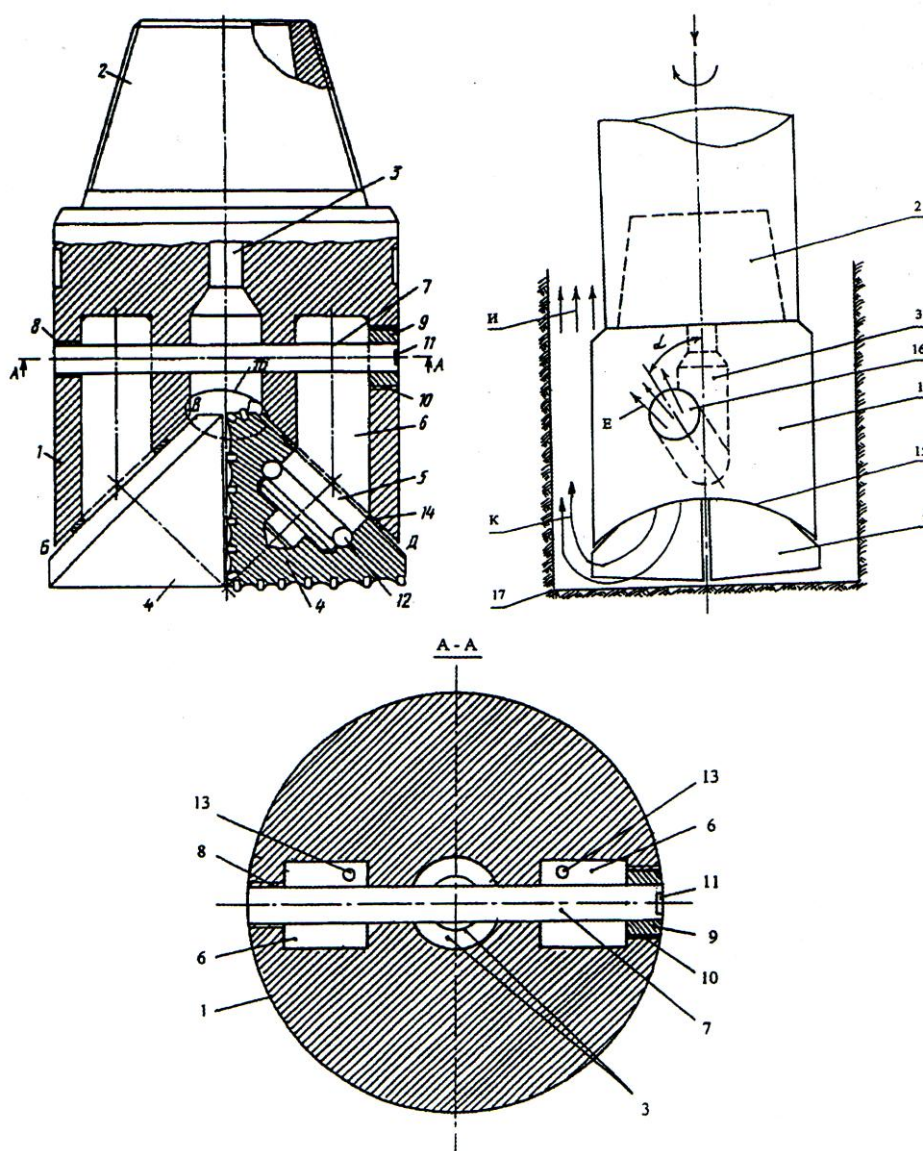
Схема двухшарошечного разборного долота со сменными шарошками: 1 – корпус; 2 – ниппель; 3 – каналы; 4 – шарошка; 5 – цапфа; 6 – хвостовик; 7 – крепежный стержень; 8, 10 – отверстие; 9 – крепежная гайка; 11 – выемка в гайке; 12 – замковый подшипник; 13 – продувочные каналы; 14 – прокладочная шайба; 15- технологический вырез; 16 – цилиндрический канал; 17 – периферийная зона забоя
